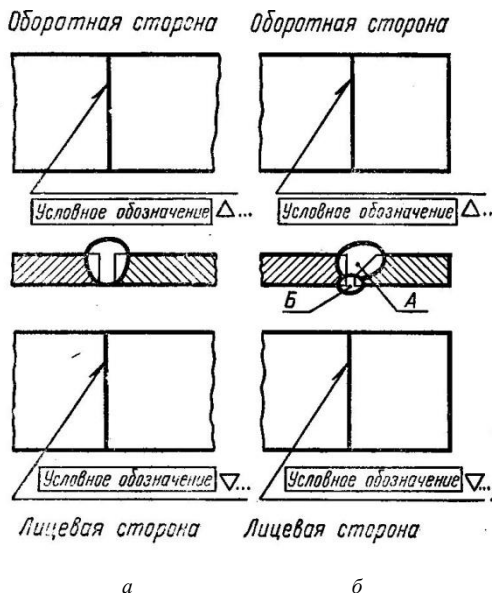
Простановка условного обозначения шва: а – односторонний шов; б – двусторонний шов; (А – шов основной; В – шов вспомогательный)
